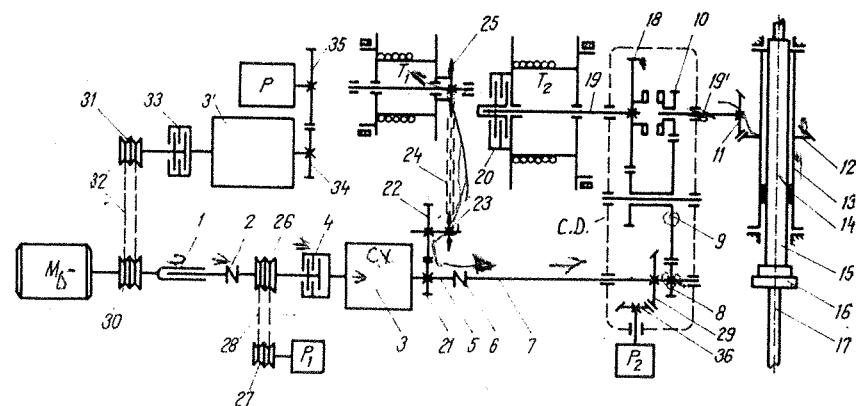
Schema cinematică a sondezei SG-300 acționată cu motor Diesel.
